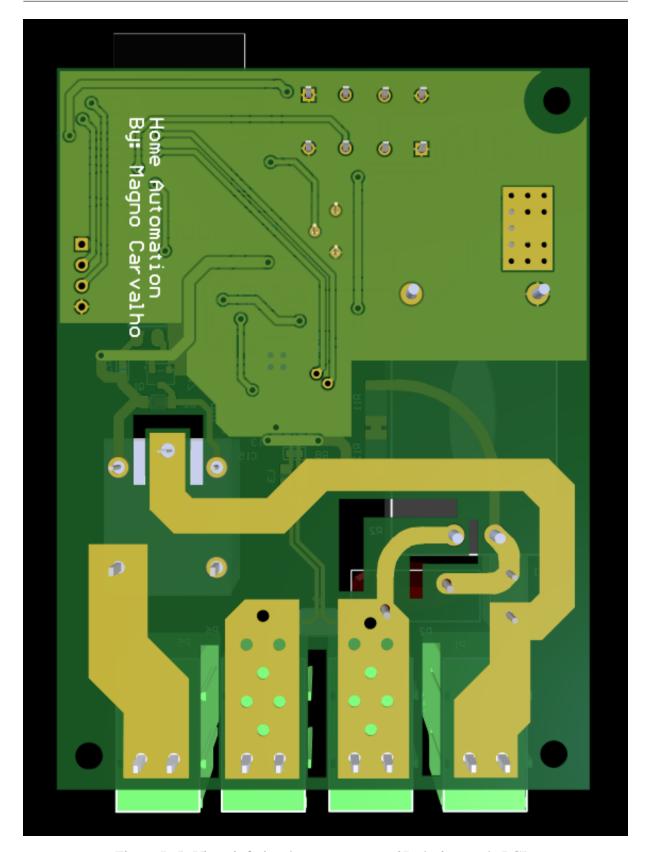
Visão inferior da representação 3D do layout da PCB.
